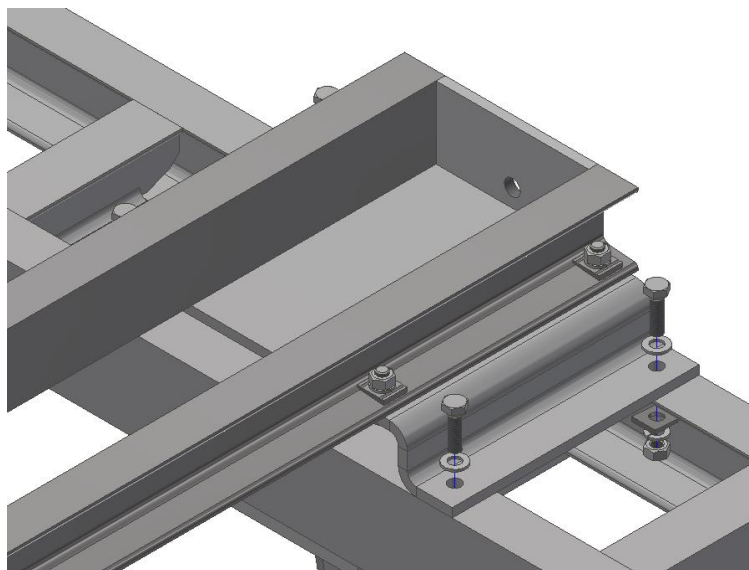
Etapa 7: Montagem do braço central e chapa de fixação à base de assentamento
